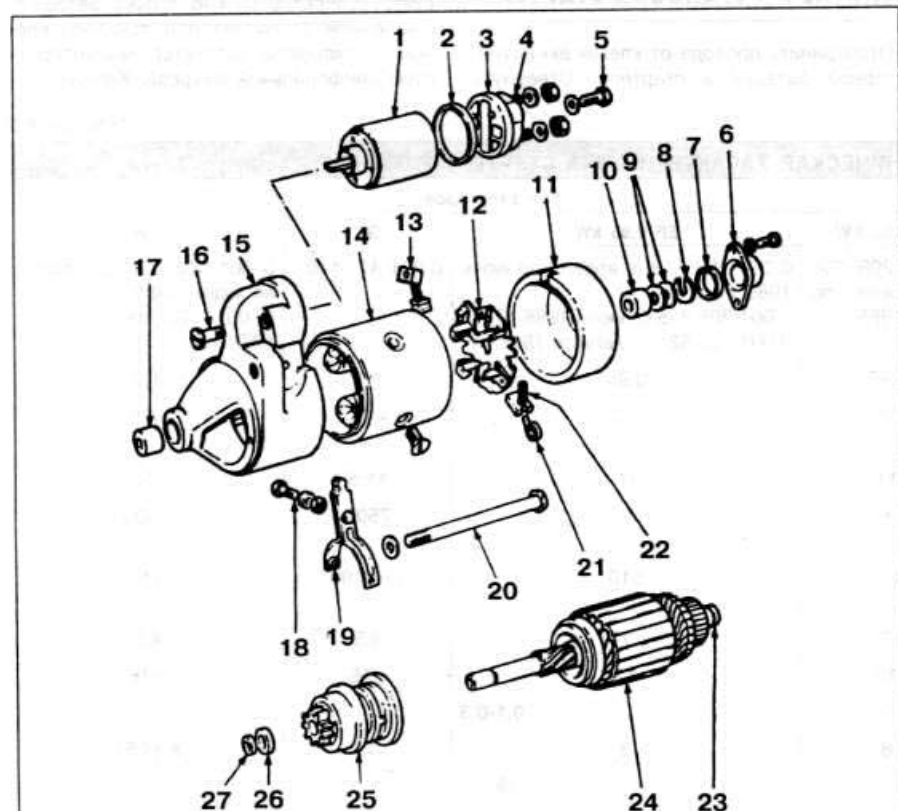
Детали стартера типа GF 1,1 kW:
